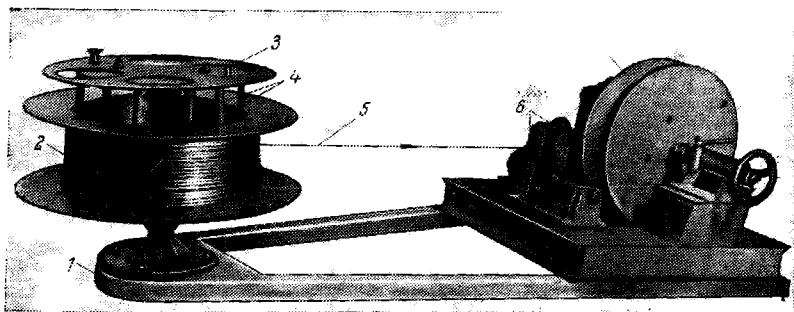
Устройство для перемотки проволоки для колец велосипедных покрышек: 1 — стойка; 2 — бухта с проволокой; 3 — диск; 4 — спицы веретена; 5 — проволока; 6 — распределительное устройство; 7 — катушка с перемотанной проволокой.
